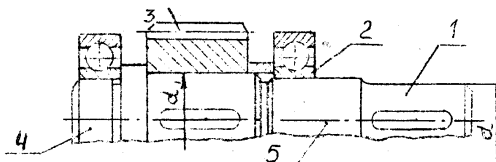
Вал в сборе: 1-вал; 2-подшипник; 3-шестерня; 4-шип; 5-шейка
